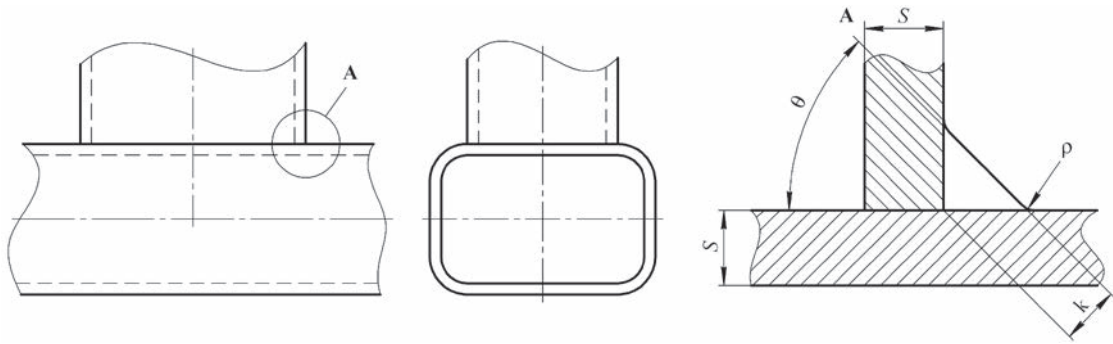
Схема Т-образного сварного соединения прямоугольных труб
